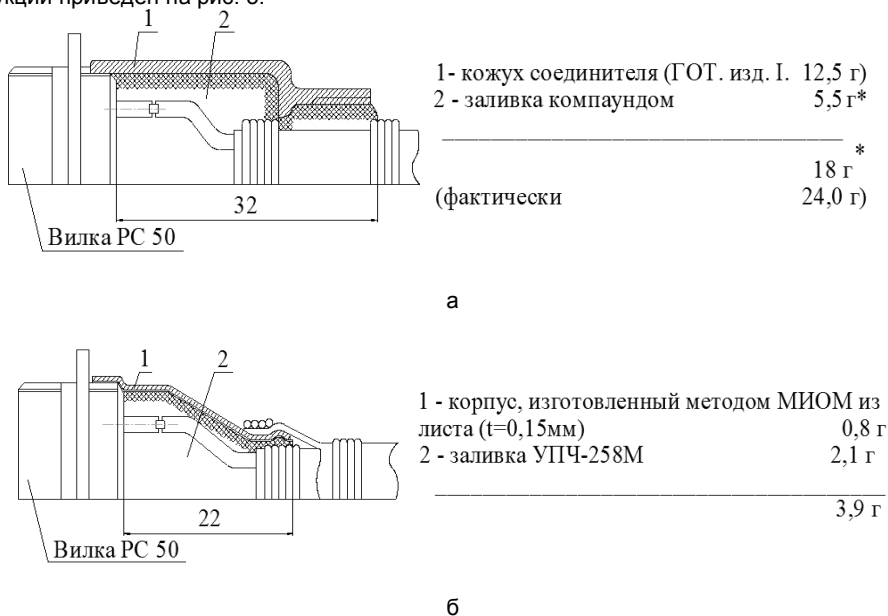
Сравнительный анализ различных конструкций заделки корпуса в штепсельный разъем:
